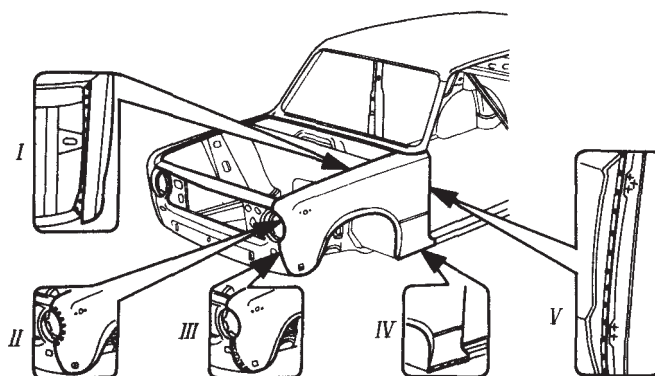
Приварювання переднього крила (місця зварювання вказані точками)
